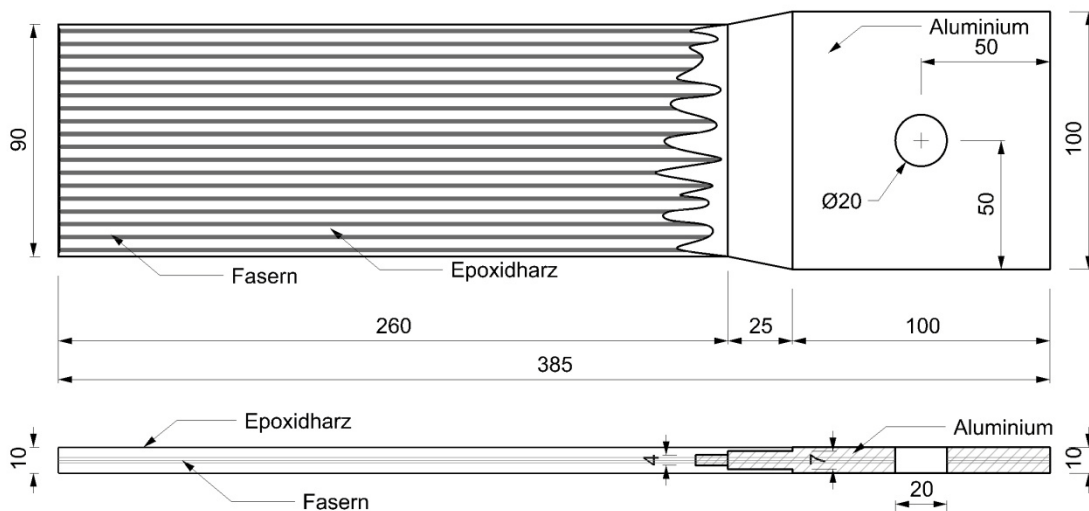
Abmessungen der Prüfkörper für Bauteilversuche in Draufsicht (oben) und Längsschnitt (unten) (Angaben in mm)
